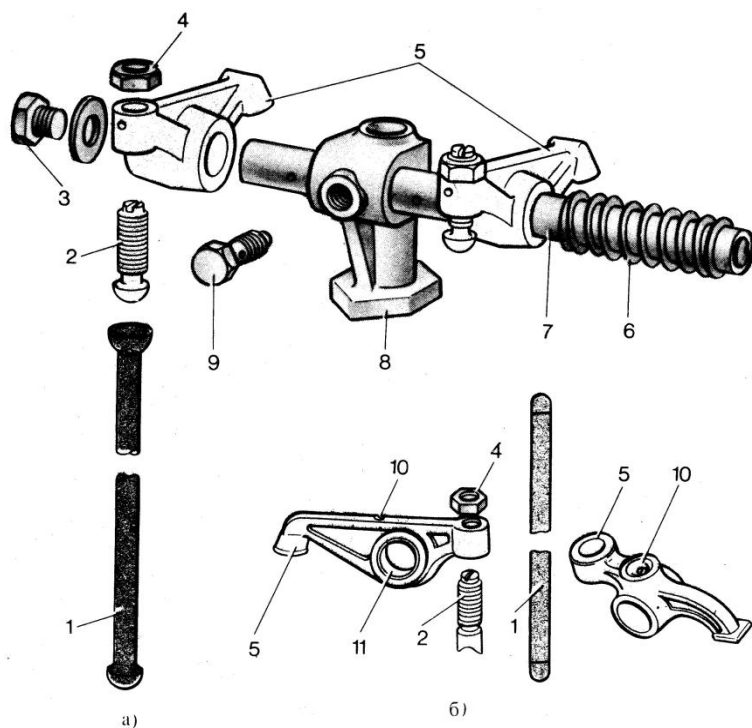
Коромысла и штанги: а - с углублением в наконечнике штанги, б - со сферическим наконечником штанги; 1 - штанга, 2 - регулировочный винт, 3 - заглушка, 4 - контргайка, 5 - коромысло, 6 - пружина, 7 - ось (валик) коромысел, 8 - стойка, 9 - болт - штуцер подвода масла к клапанному механизму, 10 - отверстие для выхода масла, 11 - втулка
